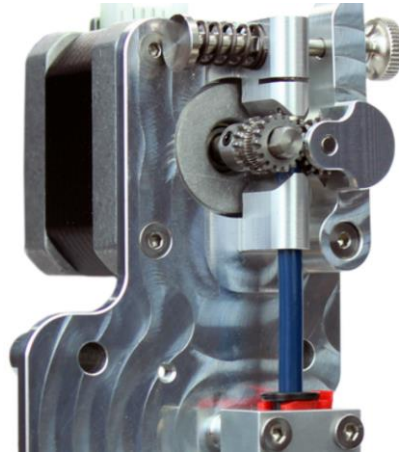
Motor de passo e engrenagens na extrusora[22]
